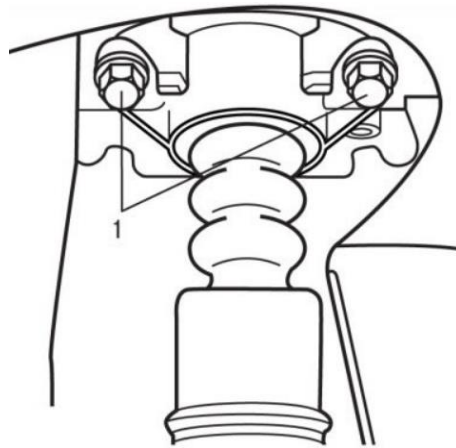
Розташування болтів 1 верхнього кріплення амортизатора
